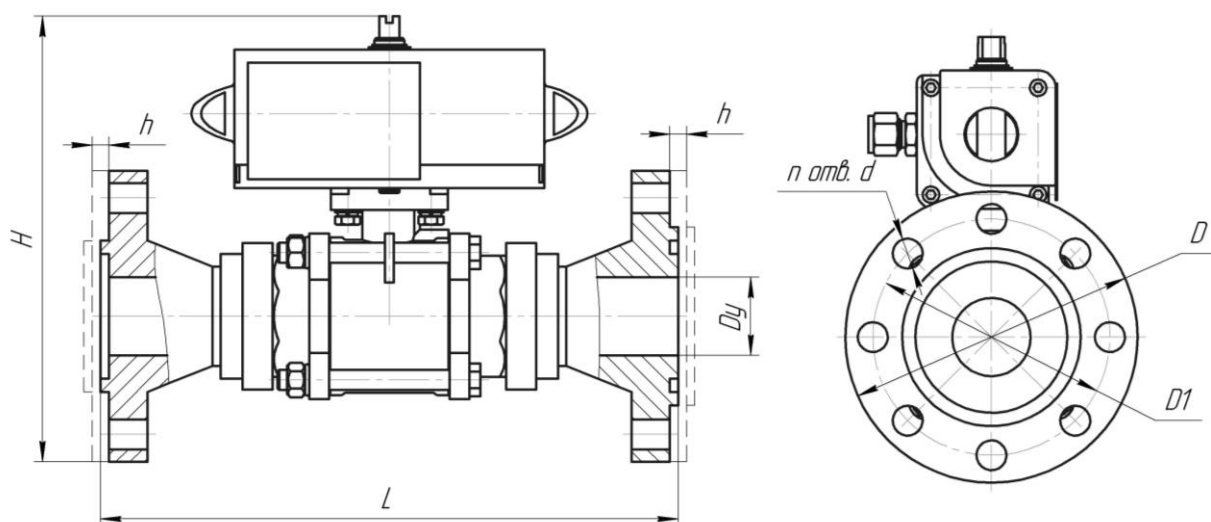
Габаритный чертеж устройства РУС-Ш с приводом из алюминиевого сплава без пускового узла
